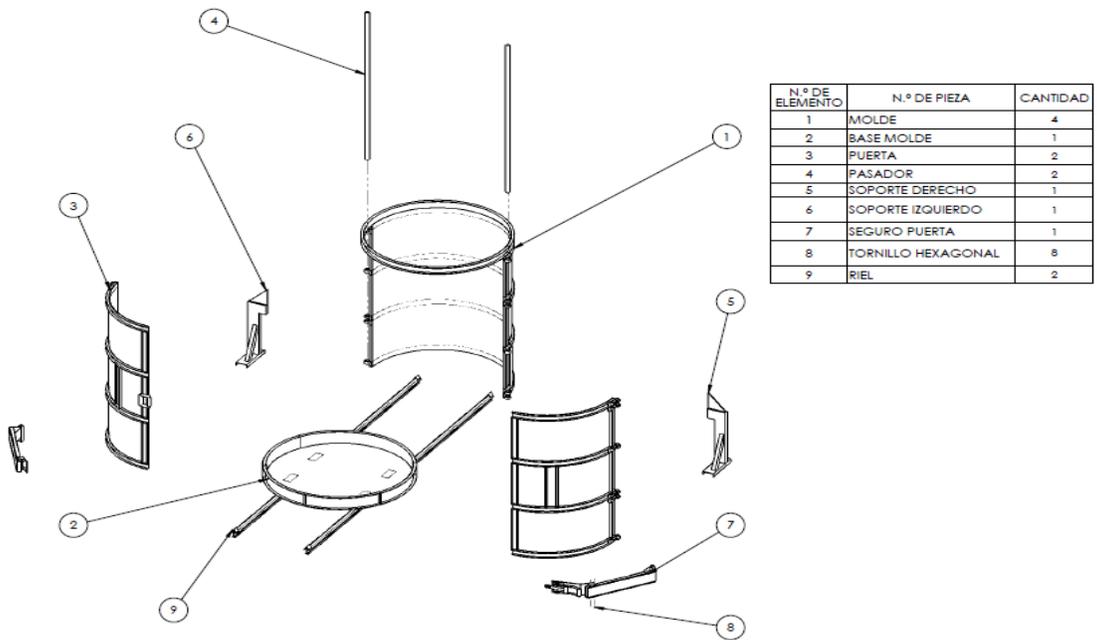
Despiece del diseño del molde cilíndrico de espuma
